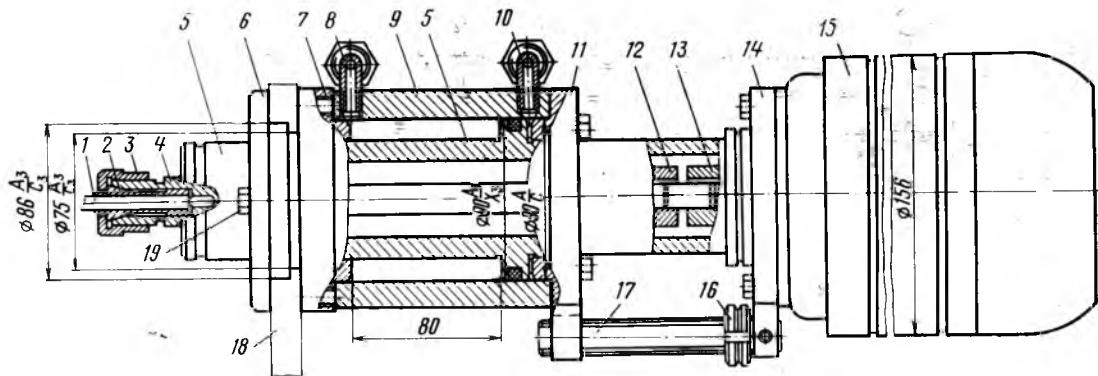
Универсальная сверлильная головка с пневмоподачей
